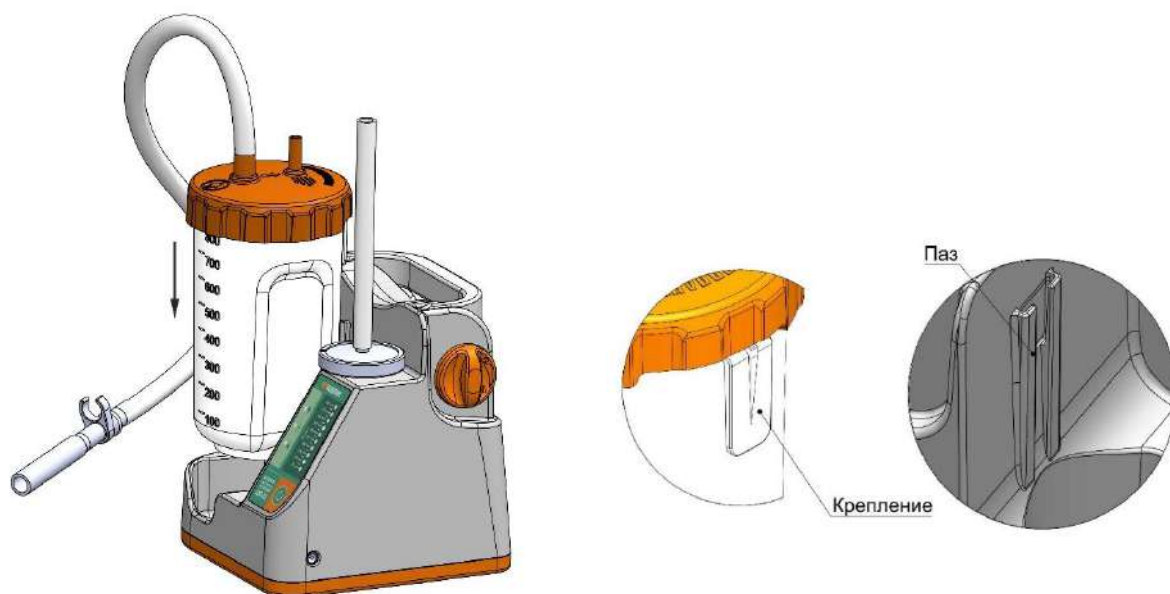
Установите контейнер-сборник в штатное место корпуса аспиратора, совместив крепление на контейнере с ответным пазом на корпусе
